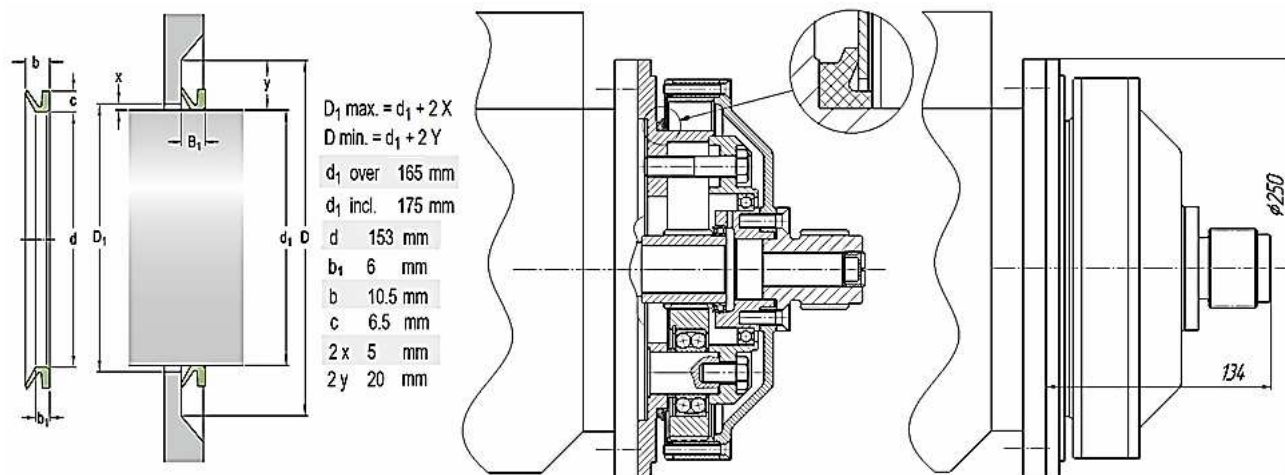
Усовершенствованный одноступенчатый многопоточный зубчатый редуктор
